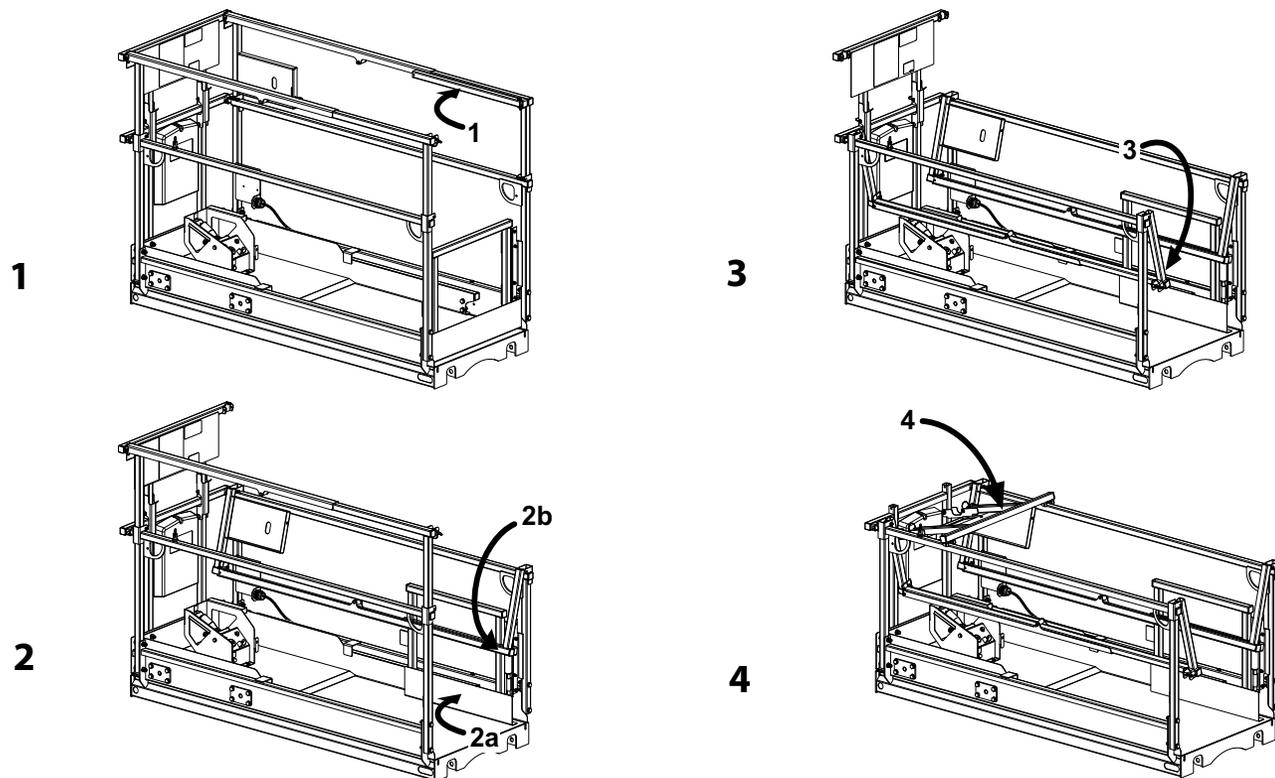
Barandillas de la plataforma - Secuencia de plegado - 6RS (CE solamente)
